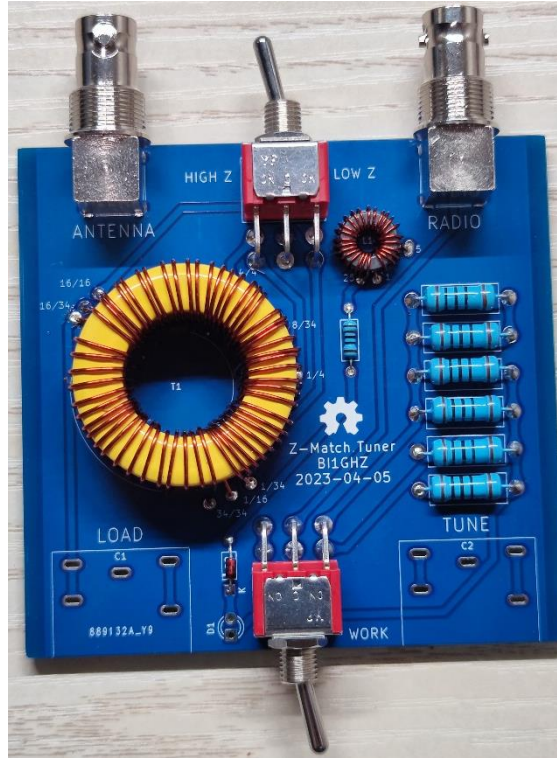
将绕好的 L2 焊接到 PCB 上
